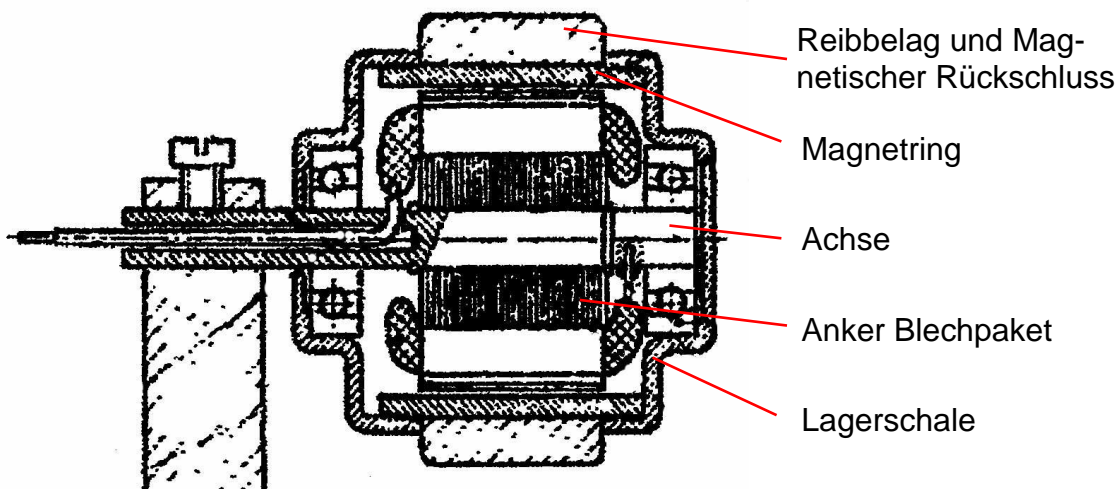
Querschnitt einer Dynamoausführung mit genutetem Blechpaket
